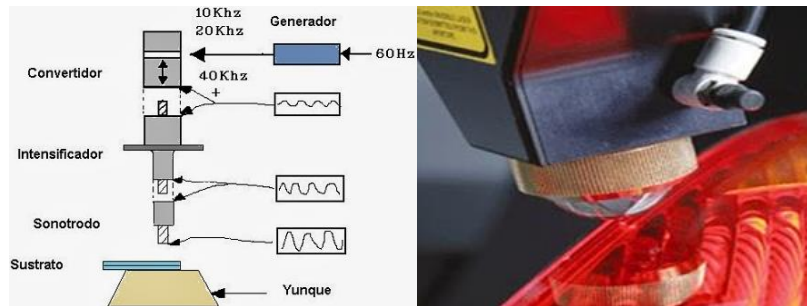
Equipo utilizado en la soldadura por ultrasonido [10].
